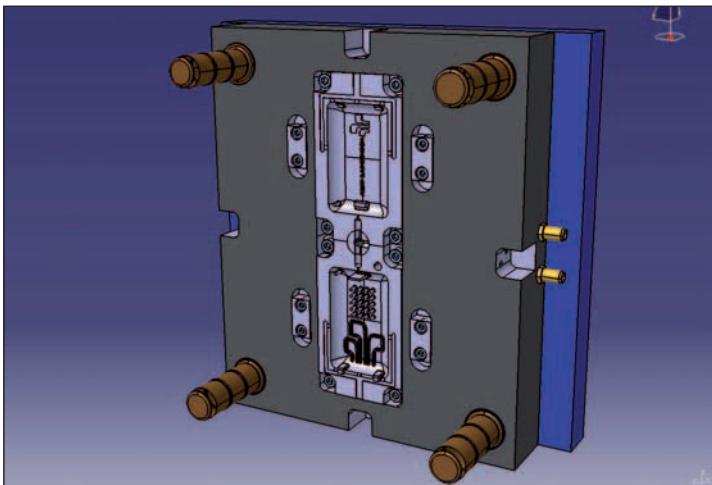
(2): 3D-Entwurf Kunststoffspritzgusswerkzeug (Düsenseite)
